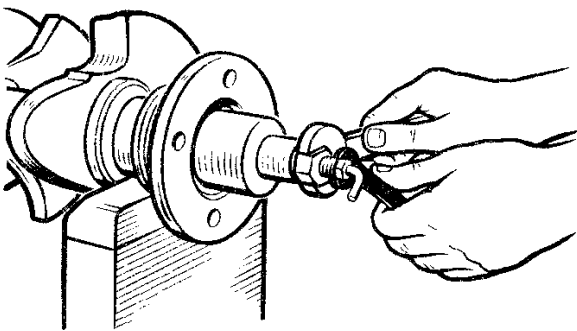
Выпрессовка подшипника первичного вала коробки передач из коленчатого вал
